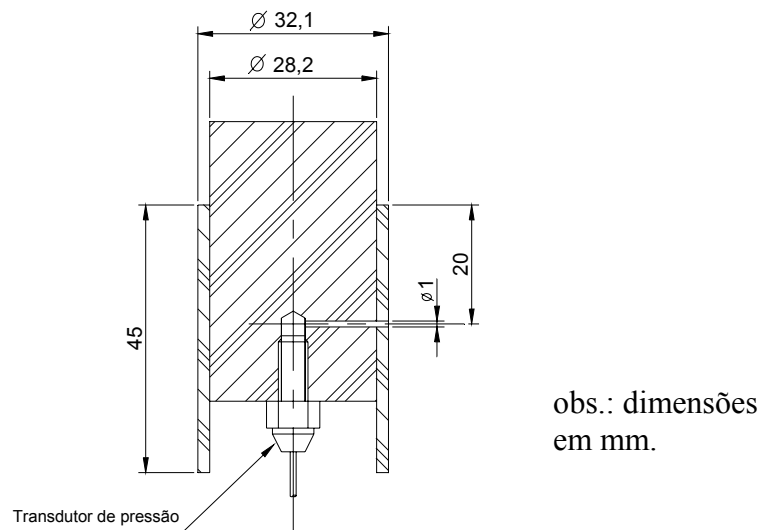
Montagem do sistema de fixação e posicionamento do transdutor de pressão
